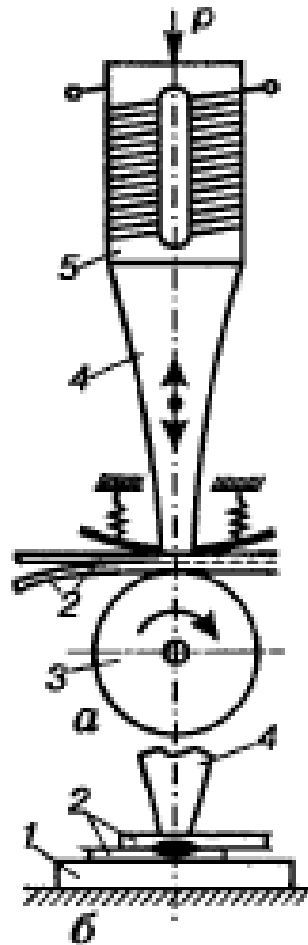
Схеми ультразвукового зварювання пластмас
